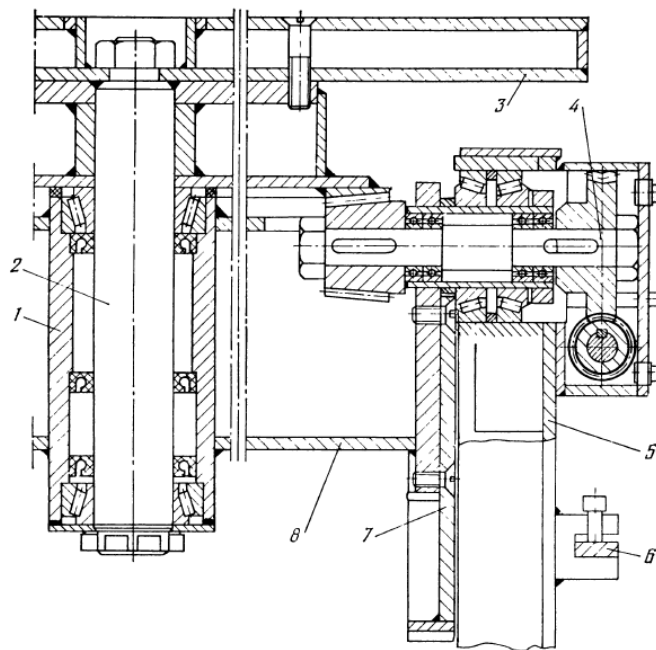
Зварювальний маніпулятор фірми “Аронсон”
